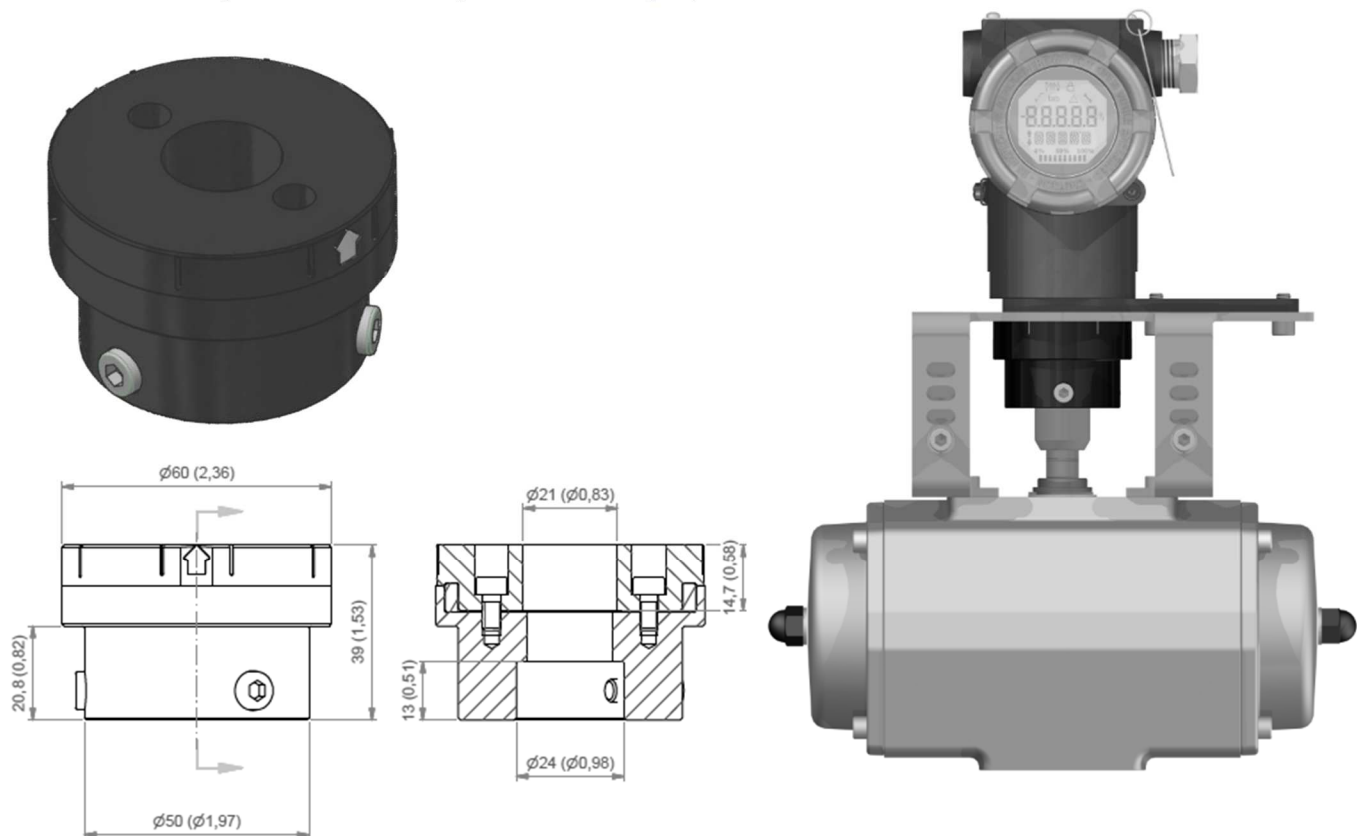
Dimensional e montagem do ímã rotativo.
